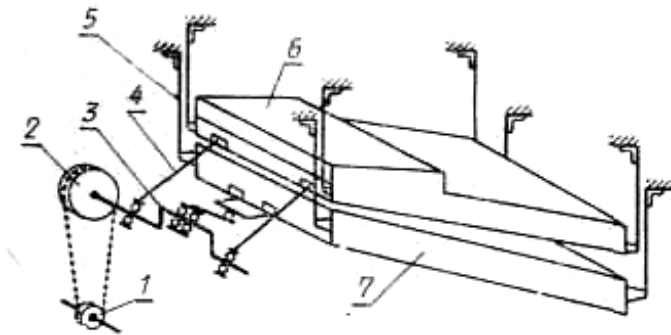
Кінематична схема приводу ситового корпусу: 1, 2 - шківів; 3 - ексцентриковий коливальник; 4 - тяга; 5 - плоска пружина; 6 - верхній ситовий кузов; 7 - нижній ситовий кузов
